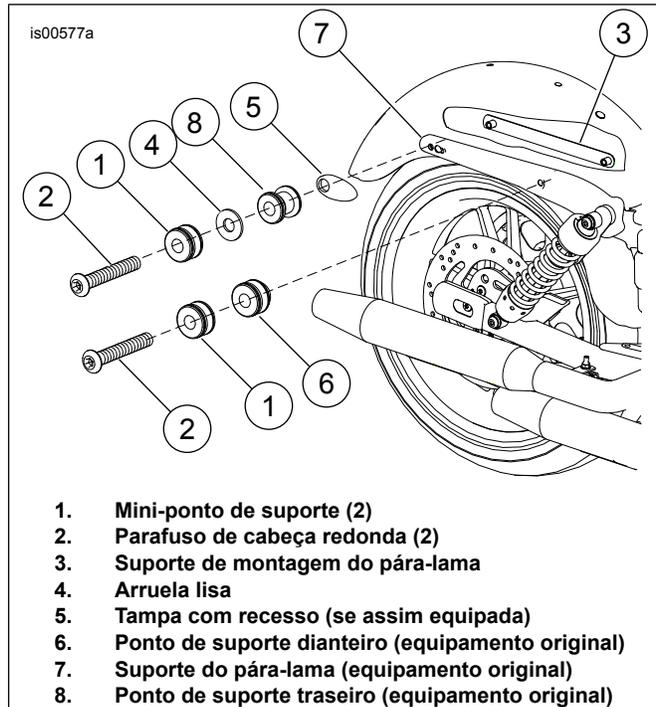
Instalação do kit de montagem do pára-lama (modelos com acessórios removíveis)
